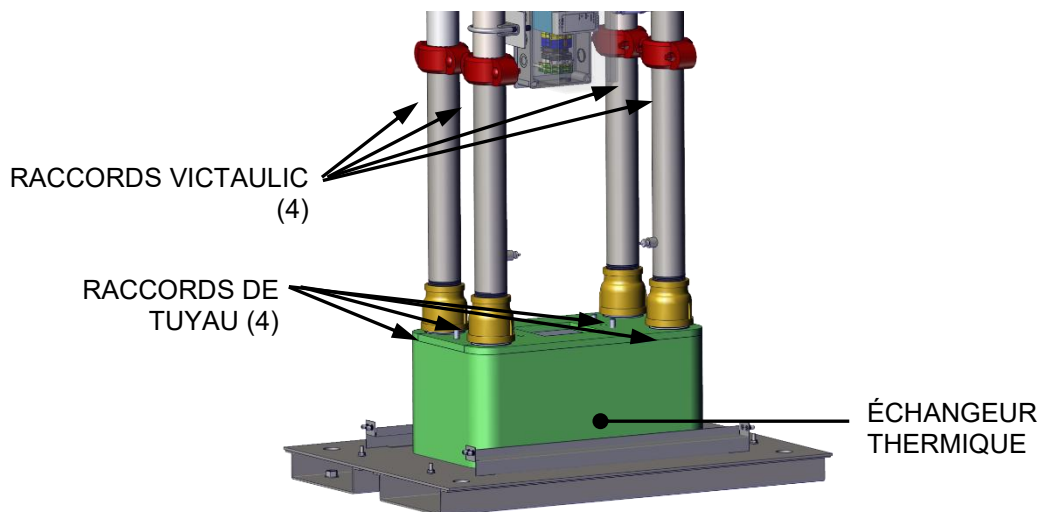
Remplacement de l'échangeur thermique – Vue avant
